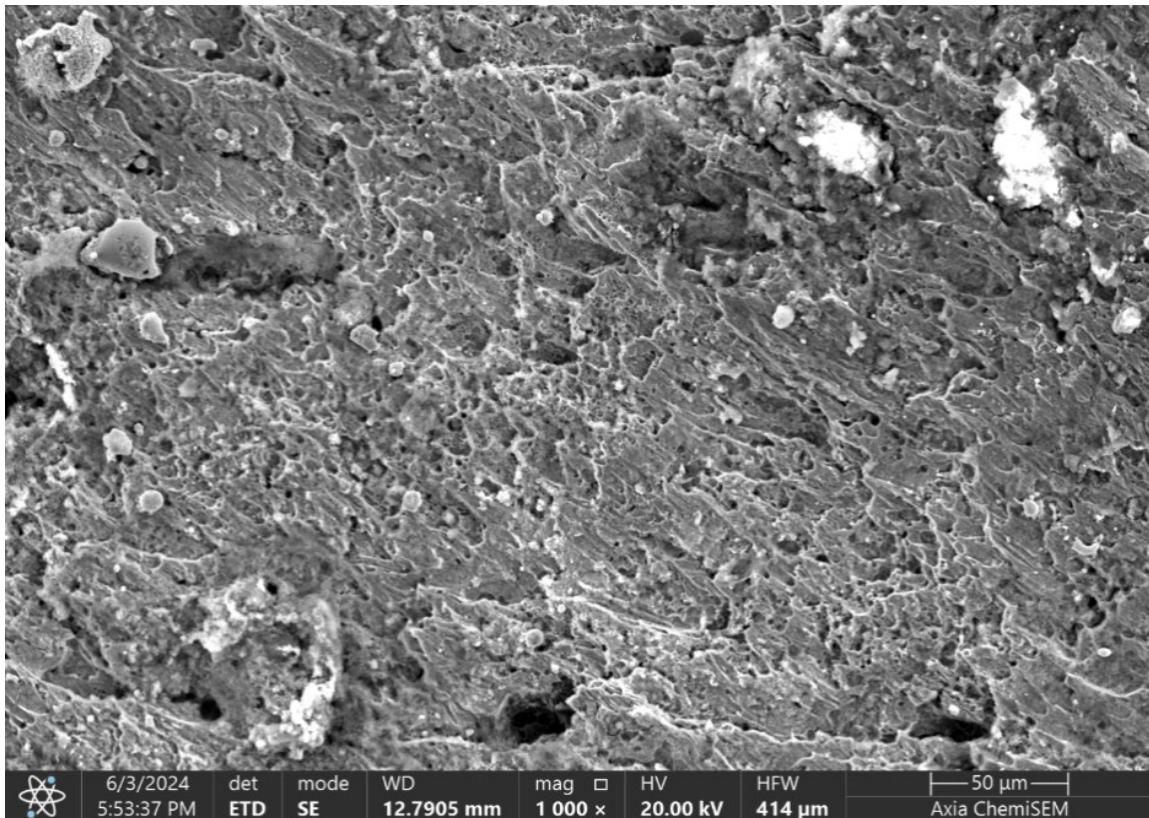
Superficie de fractura – Codo inferior – Cordón longitudinal – Línea de fusión lado metal base.
